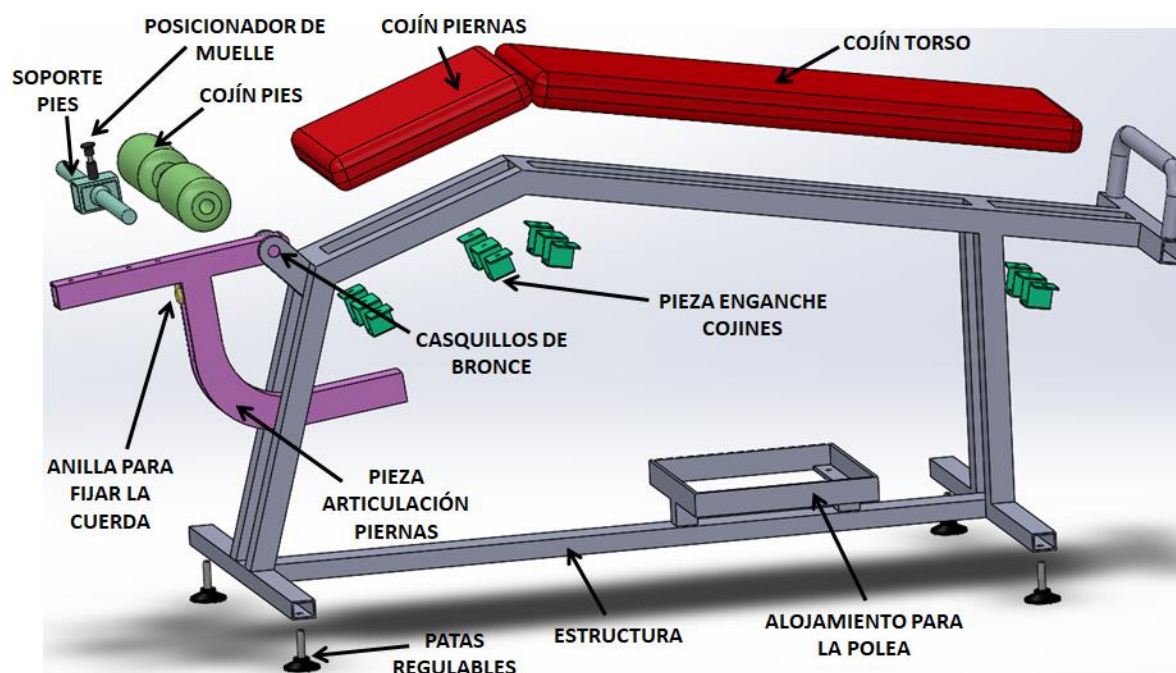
Vista explosionada de los componentes del ensamblaje del módulo Leg Curl.
